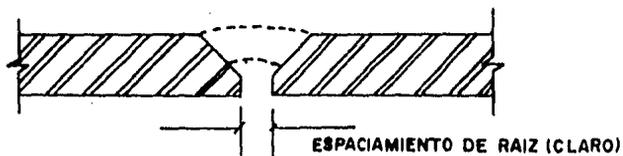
POSICIONAMIENTO PARA EFECTUAR UNA SOLDADURA A TOPE.
